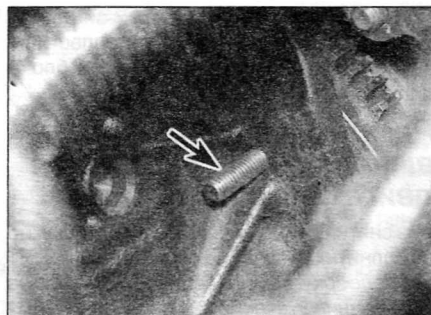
, б. Стержень (отмечен стрелкой), вставленный через фланец на блоке цилиндров в установочное отверстие в маховике
